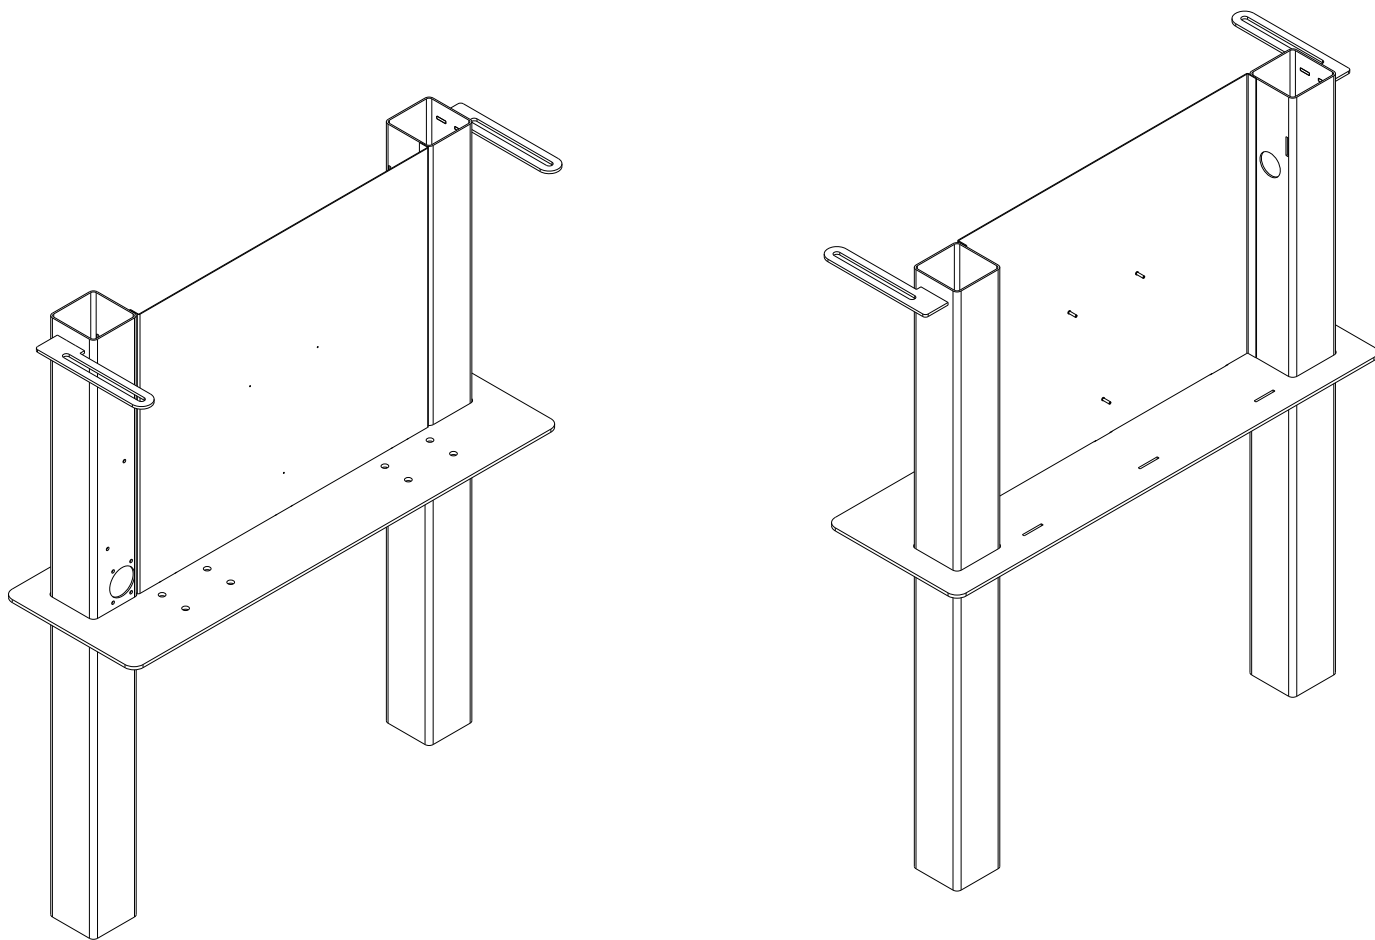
Схема сборки корпуса тумбы шлагбаума
